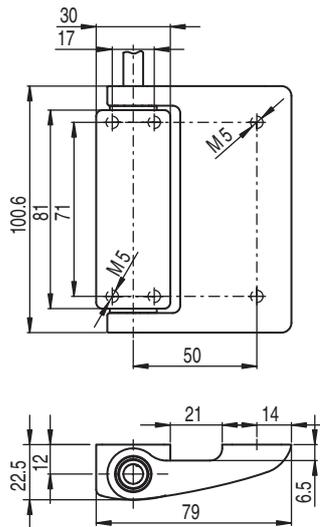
Dimensions du S410-M1CB2-T en mm
